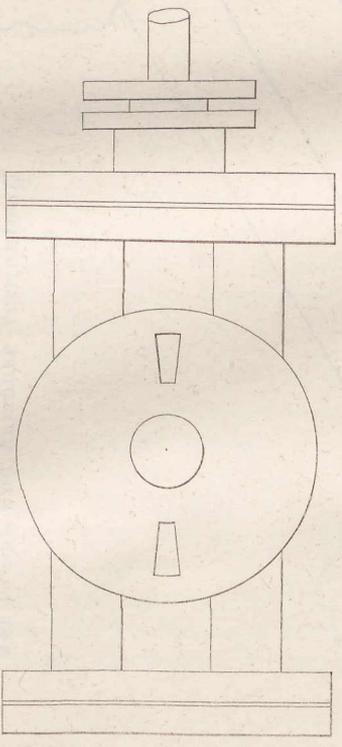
Steuerungsscheibe am Dampfzylinder.
